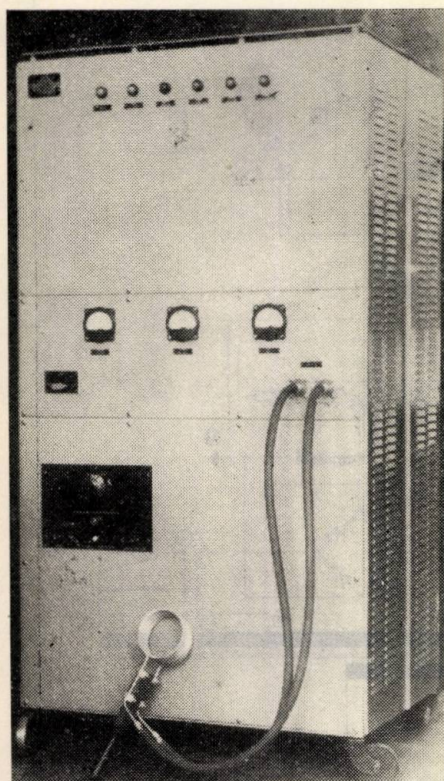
Generator de înaltă frecvență pentru încălzire prin inducție (vedere frontală).
